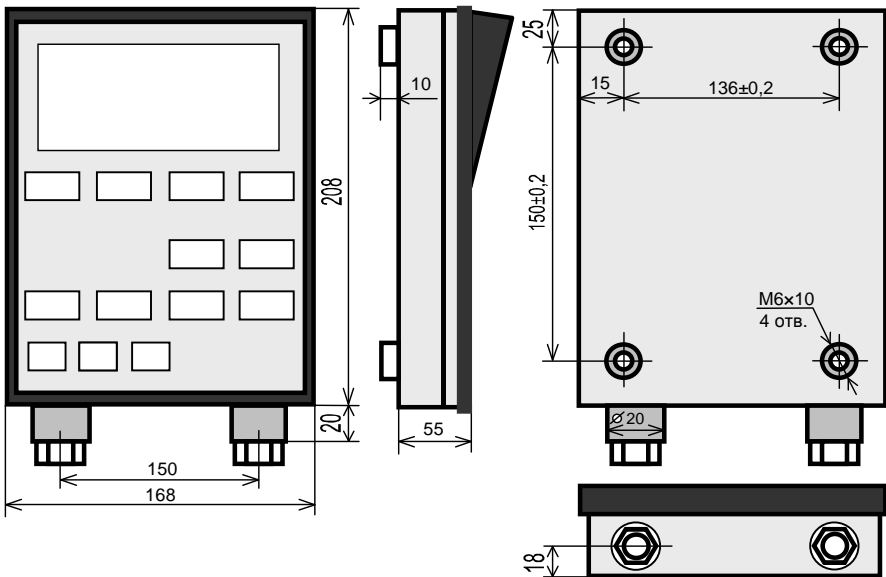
Габаритные и присоединительные размеры БОИ
